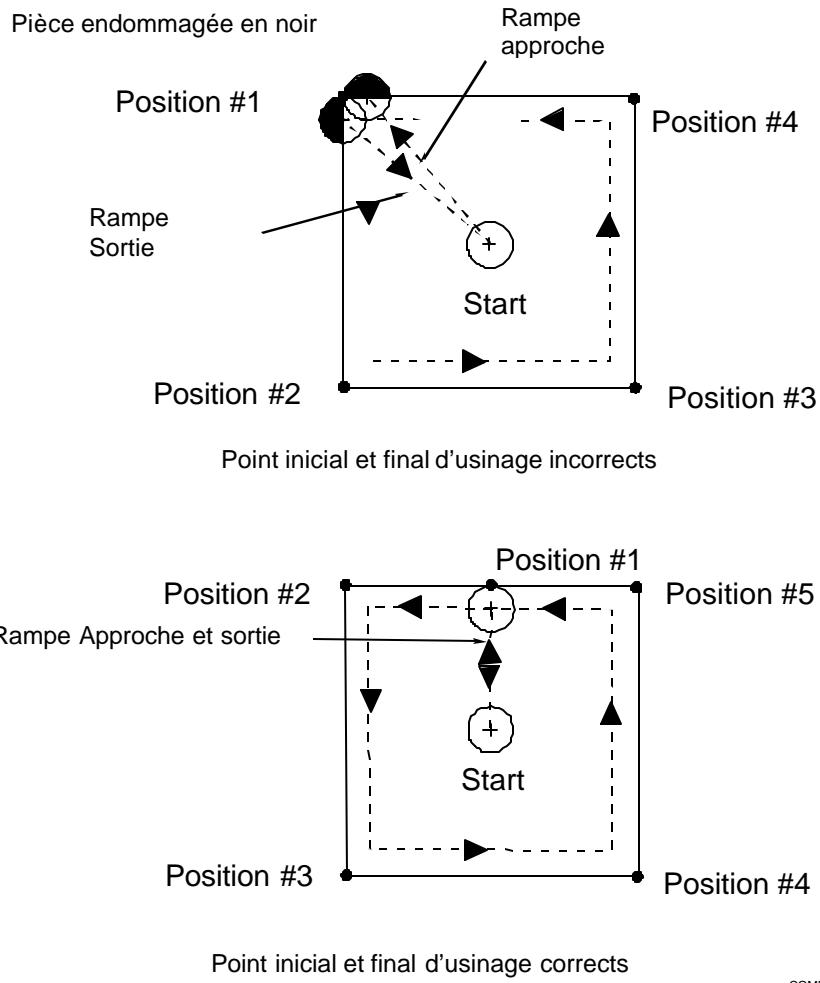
, Choix de départ et d'arrivée oblique pour le fraisage à l'intérieur d'un carré
